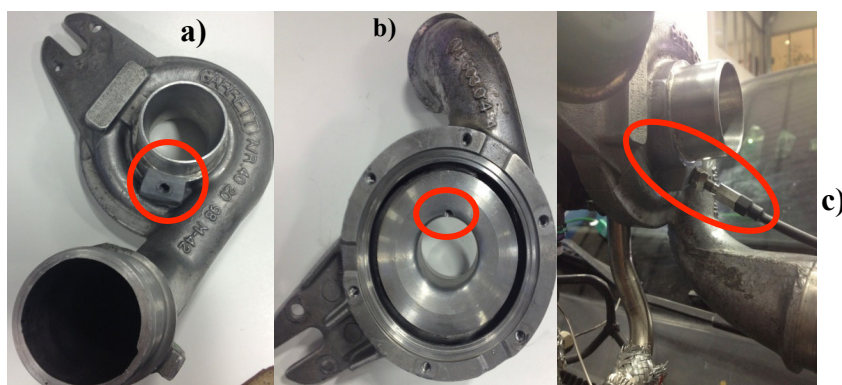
Montagem do sensor de velocidade de rotação do turbocompressor. a) Vista exterior da tampa do compressor com o furo realizado. b) Vista interior da tampa com o furo realizado. c) Sensor montado no turbocompressor.
